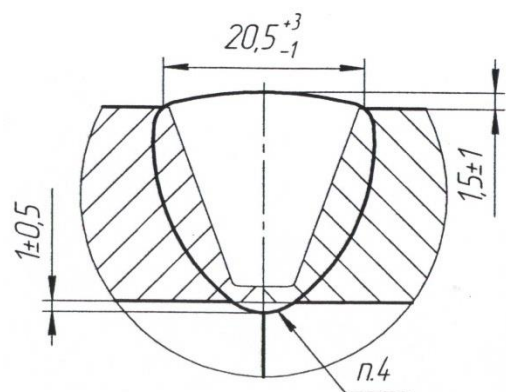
Сварной шов для толщины 19,5 мм
